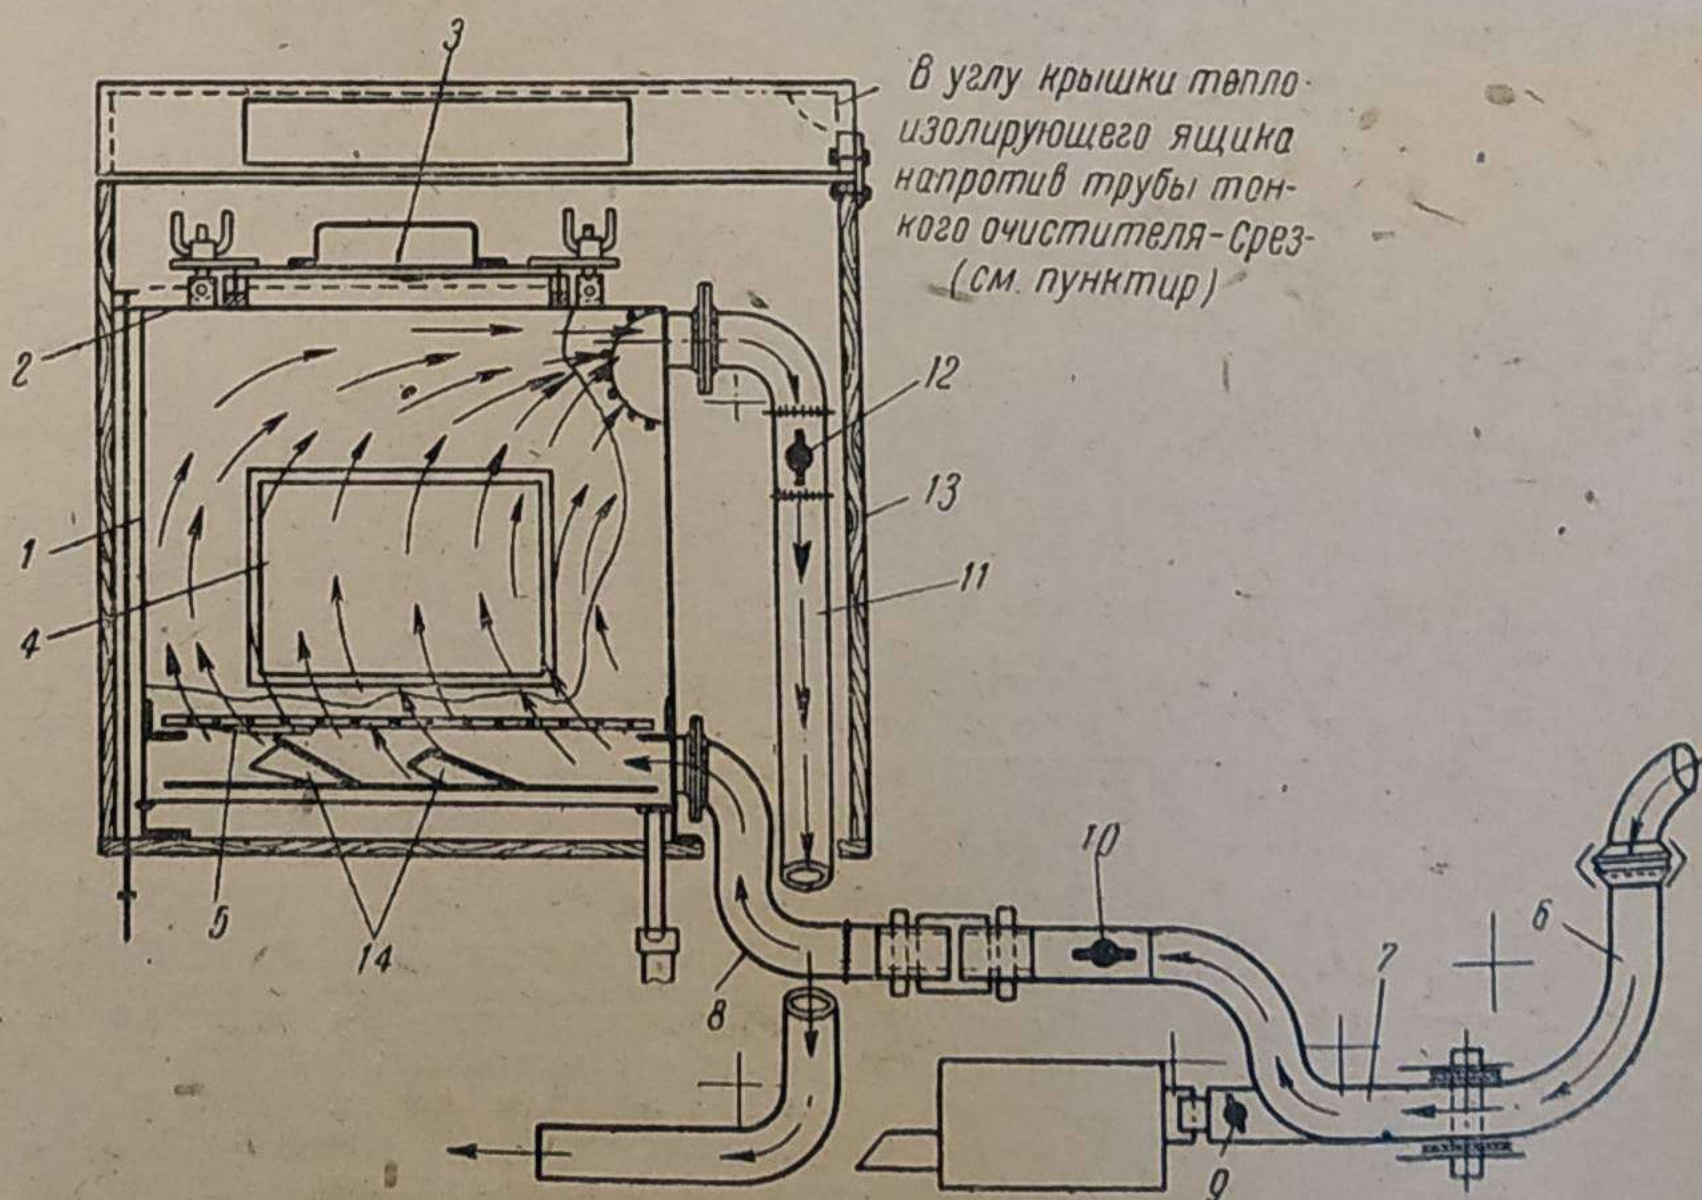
Схема сушилки для автомобиля ГАЗ-42:
